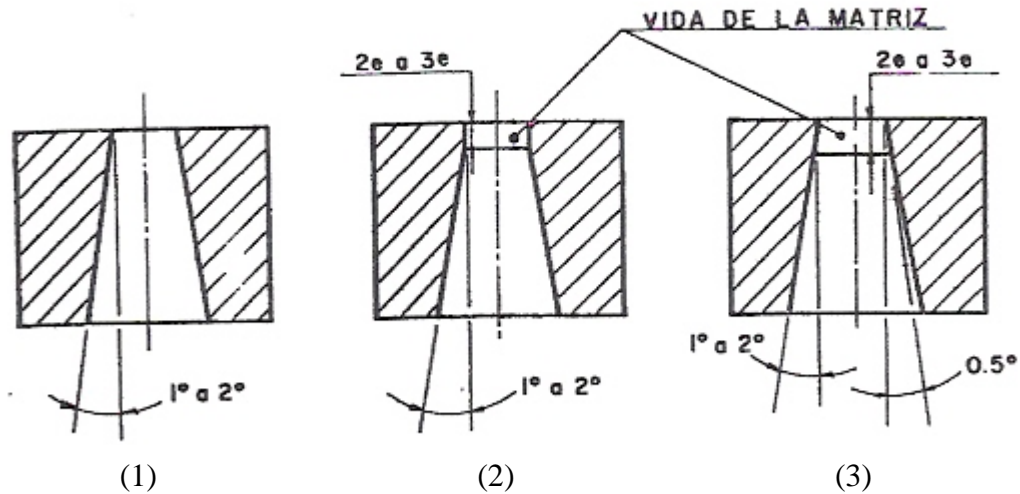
TIPO DE ÁNGULO DE ESCAPE
